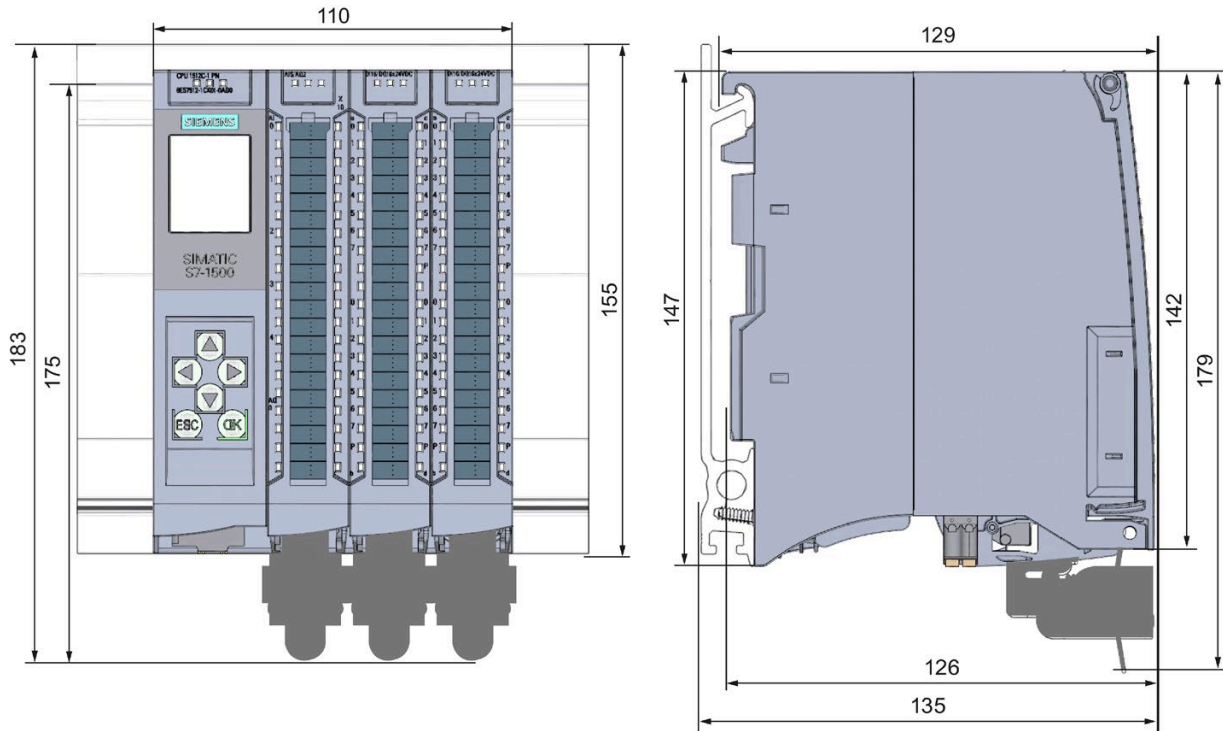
Maßbild der CPU 1512C-1 PN - Front- und Seitenansicht
